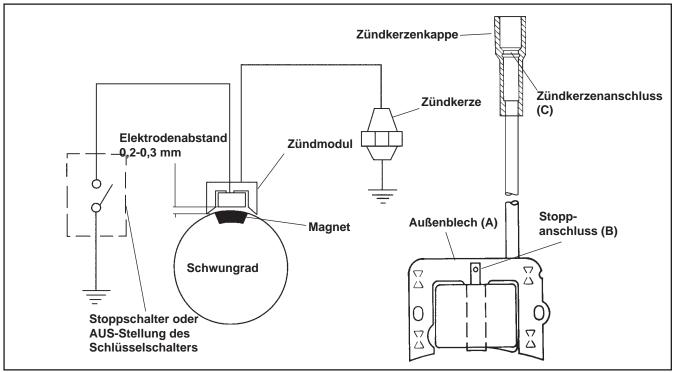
Elektronische Magnetzündanlage, CH11-15 Motore.
